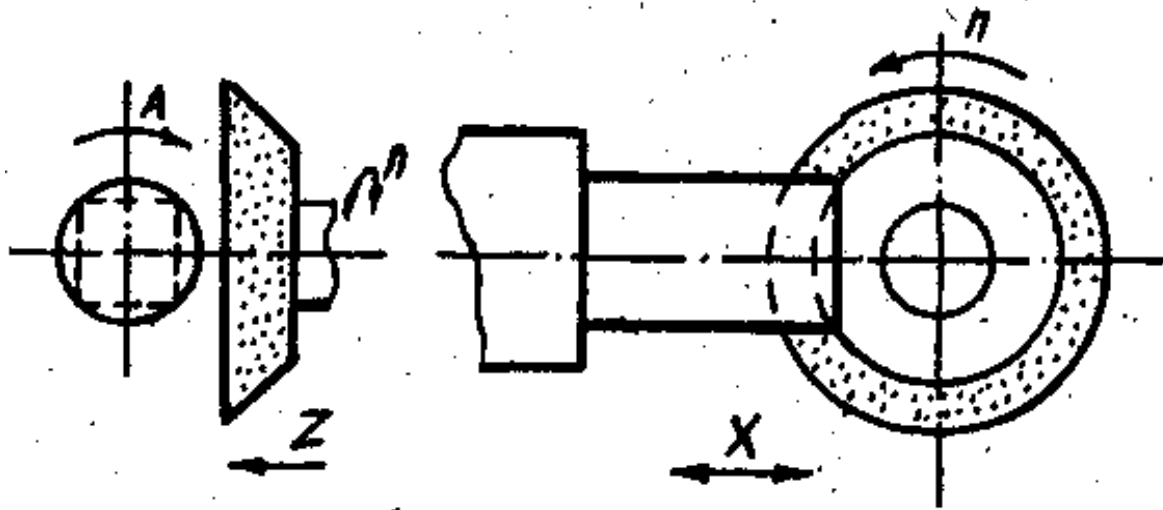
Схема обробки круглої заготовки у квадратну
